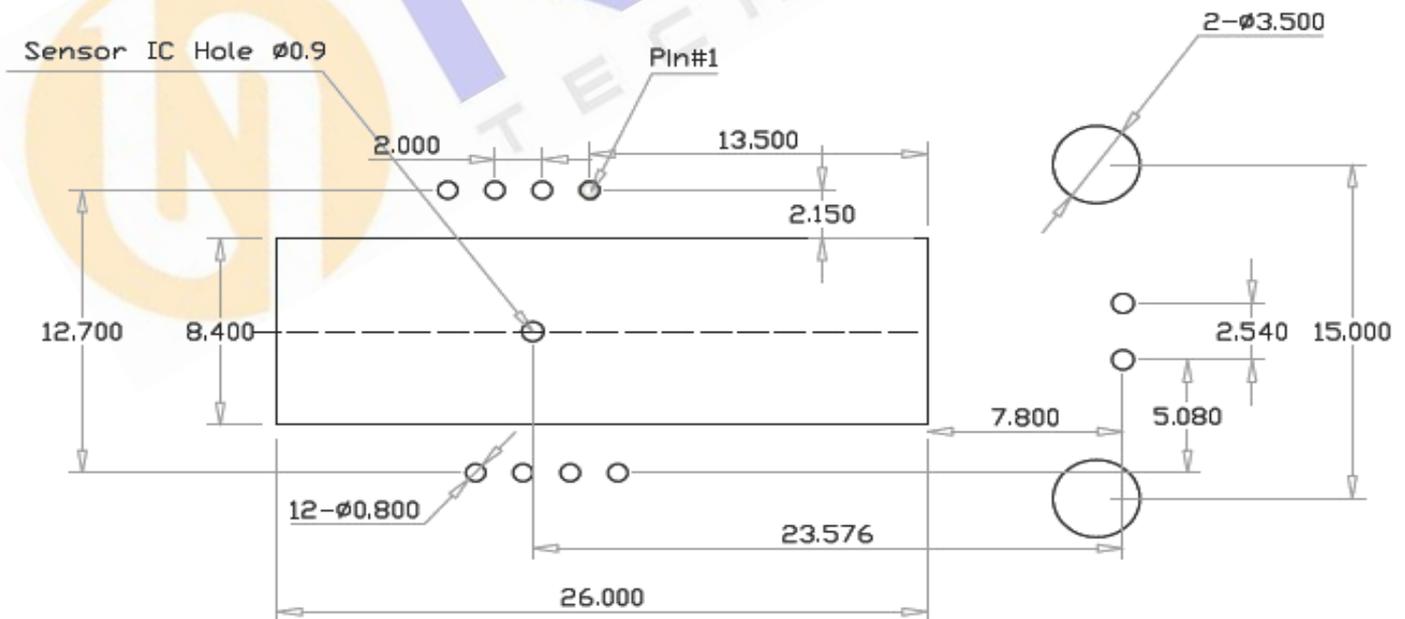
推荐 PCB 机械尺寸 (mm/inch)
